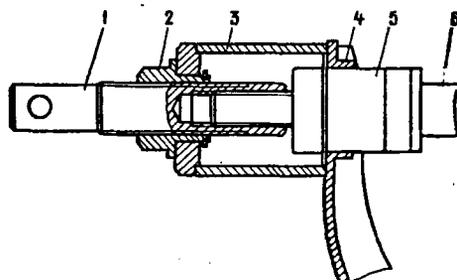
Схема выпрессовки шарнира нижнего рычага с помощью приспособления 02.7823.9500: 1 - винт; 2 - гайка; 3 - стакан; 4 - нижний рычаг; 5 - шарнир; 6 - ось нижнего рычага
